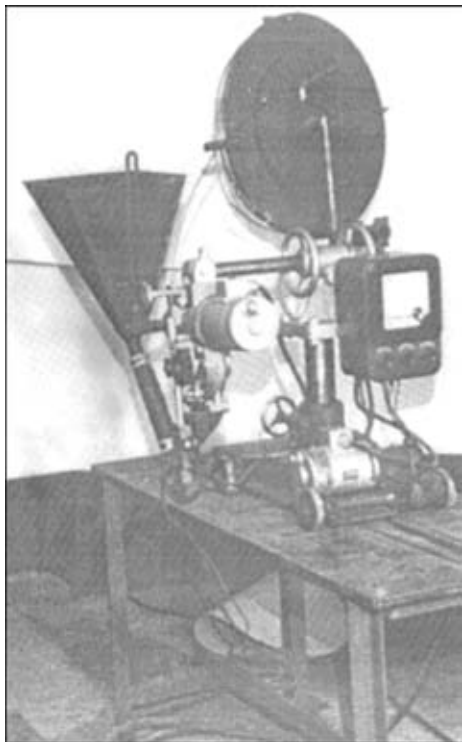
Первый автомат МАГ-1 для сварки под флюсом стыковых соединений судовых конструкций
